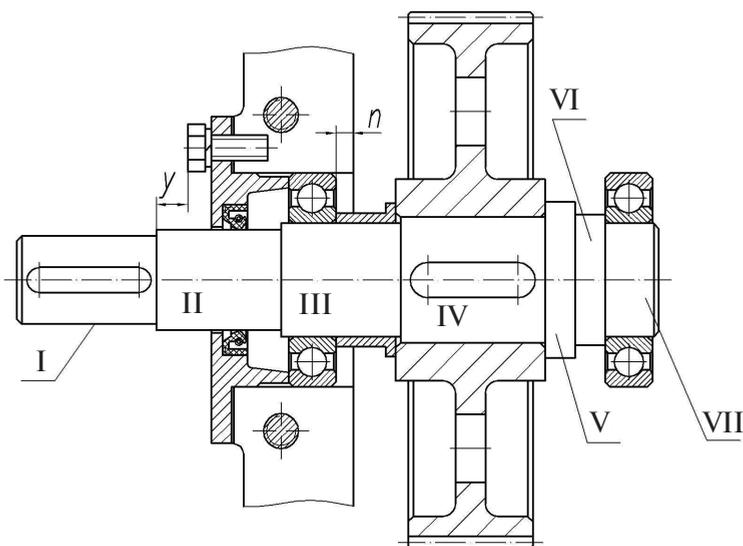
Эскизная компоновка тихоходного вала редуктора
